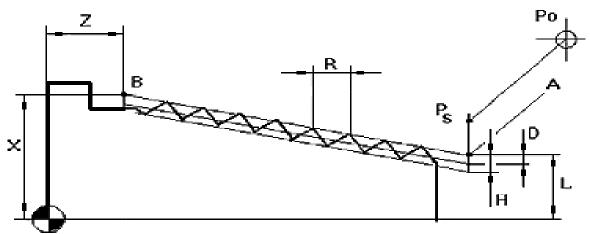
Интерпретация токарного цикла нарезания резьбы по G83: X – координата конечной точки резьбы B; Z – линейная координата конечной точки резьбы B; R – шаг резьбы (мм/оборот); L – диаметр или радиус начальной точки резьбы A; D – глубина одного прохода (толщина стружки); H – общая глубина резьбы. Примечание. X, D и H задаются в диаметральном выражении; X, L и Z – в абсолютной системе отсчета
